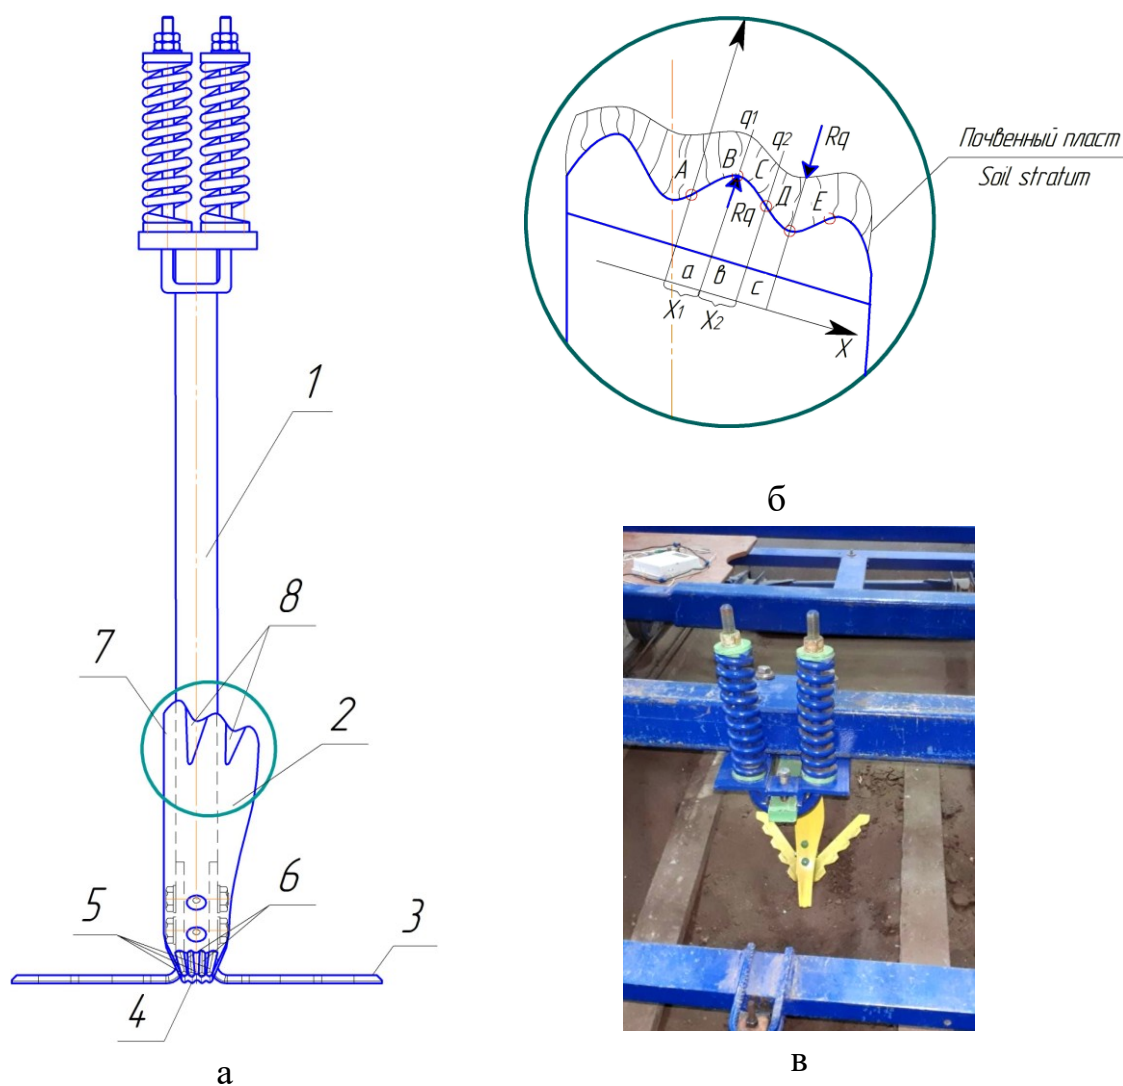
Рабочий орган стерневого культиватора: а) вид спереди; б) схема движения почвенного пласта по верхней части долота; в) натурный образец рабочего органа стерневого культиватора в почвенном канале
